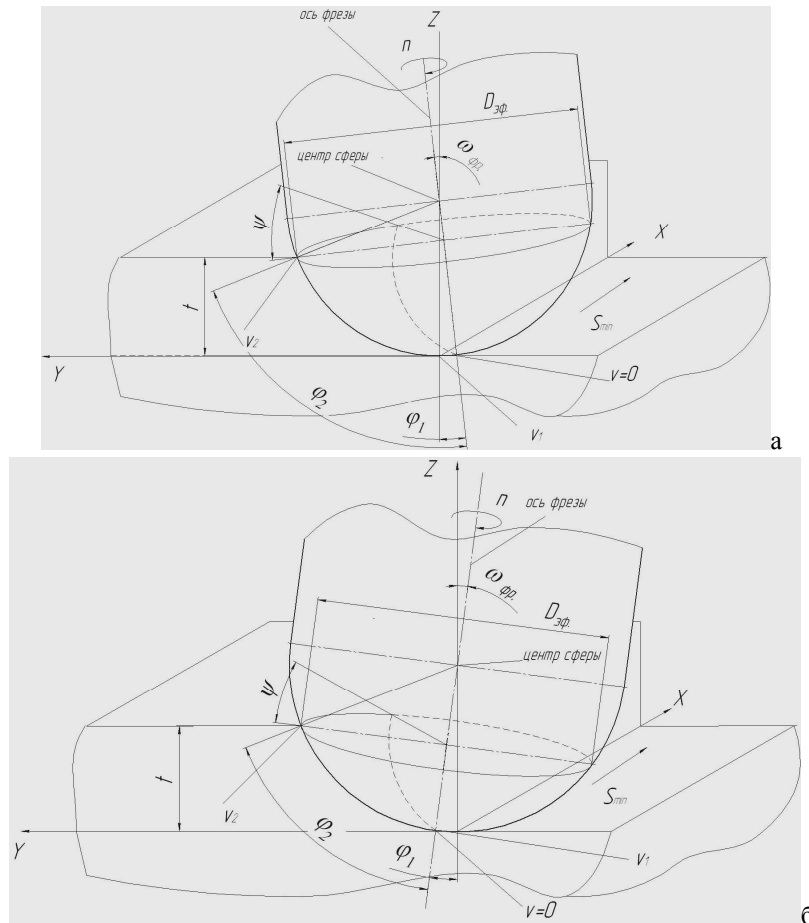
Наклон сферической фрезы в процессе работы (а – к обрабатываемой поверхности; б - от обрабатываемой поверхности)
